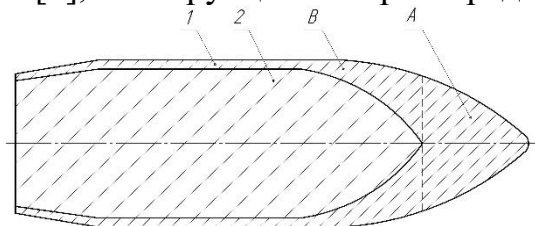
Схематическая конструкция пули: 1 - корпус; 2 - свинцовый наполнитель (сердечник); А - твёрдая хрупкая зона корпуса (носик); В - зона
